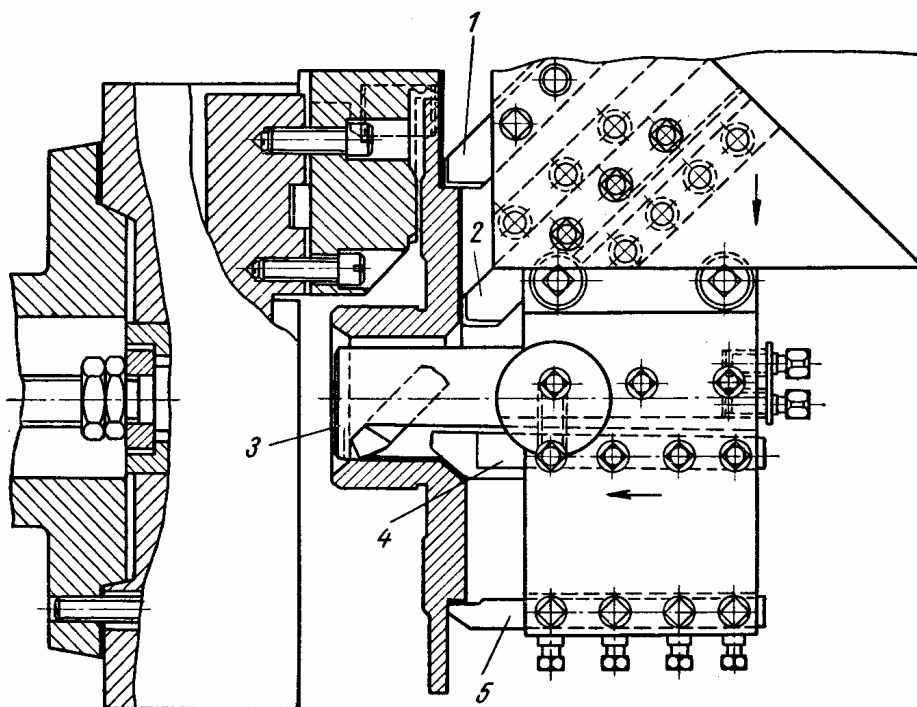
Наладка многорезцового полуавтомата для обработки крышки корпуса дифференциала автомобиля
